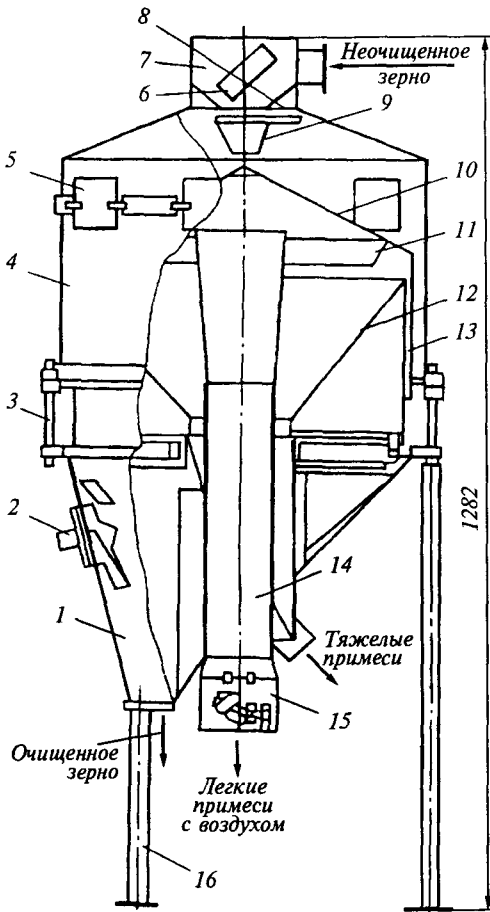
Пневматический сепаратор РЗ-БСД
